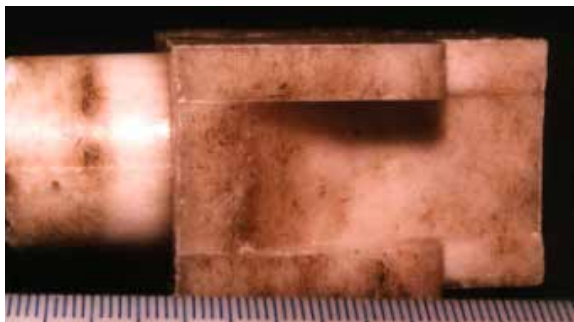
Внешний вид пористой удаляемой модели, для отливки типа «Корпус».
